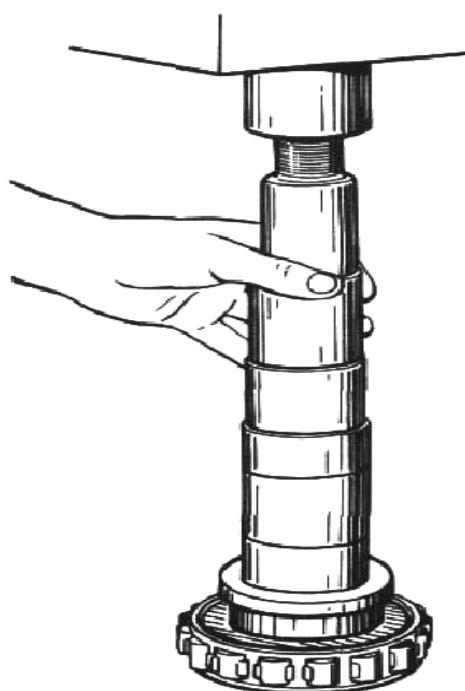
Напрессовка среднего подшипника на промежуточный вал
